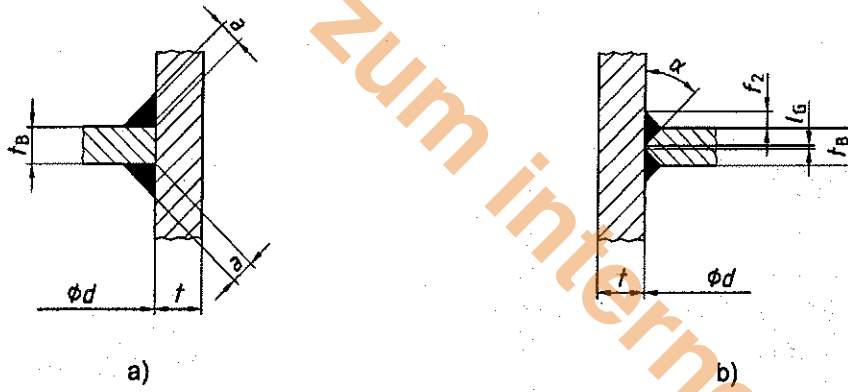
Schweißverbindung zwischen Tankwand und Boden
